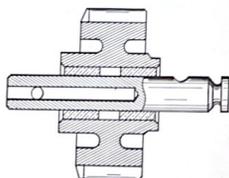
Engrane inversor de Marcha Atrás con su eje.
